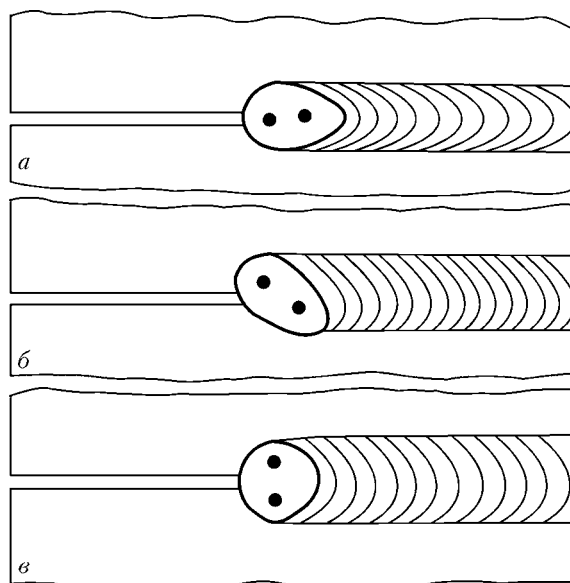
Схема расположения электродных проволок при двухдуговой сварке: а — продольное; б — под углом 45°; в — поперечное
